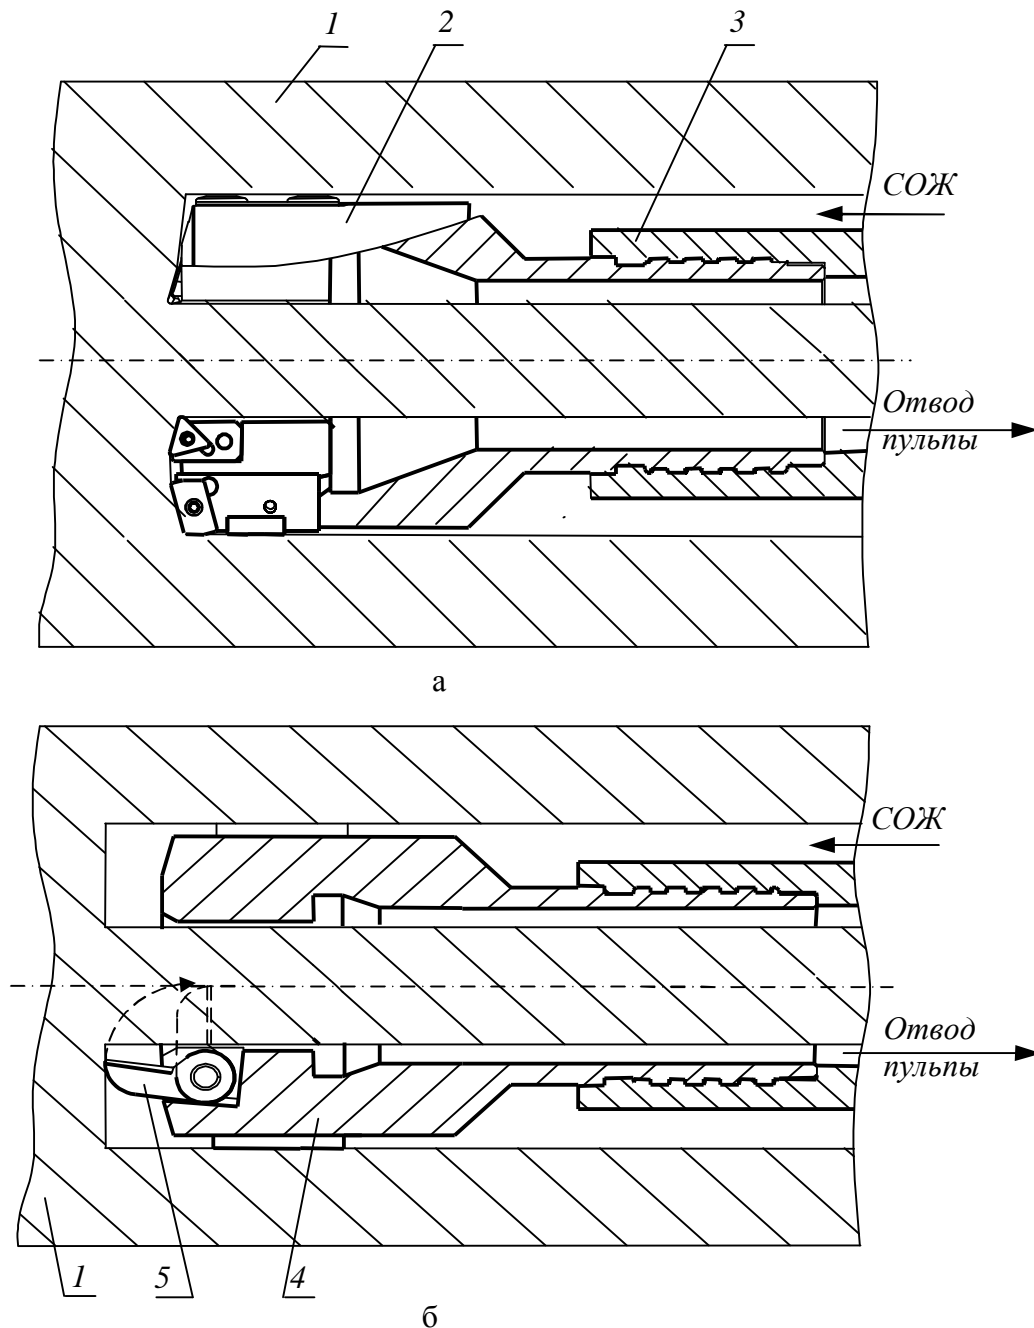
Кольцевое сверление (а) с последующей отрезкой стержня пробы (б)
